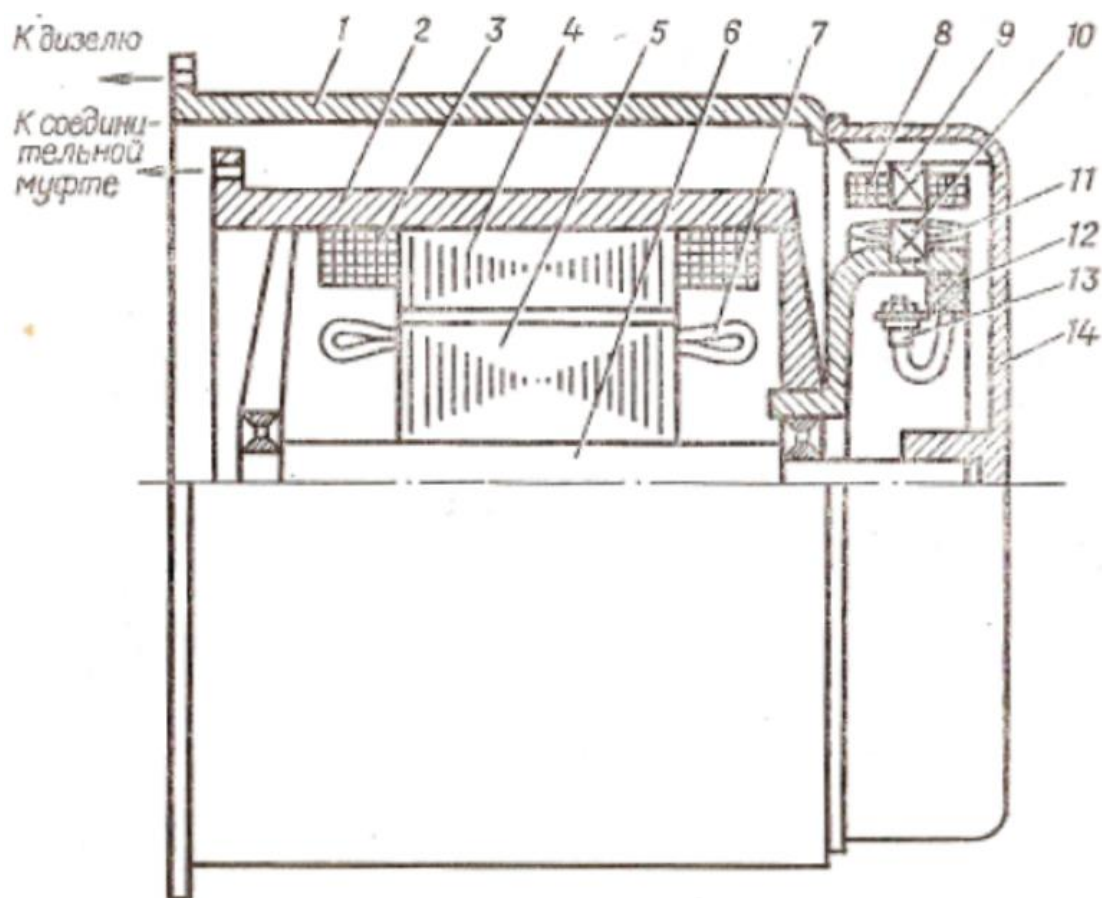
Маховичный синхронный генератор ГСМ: 1 – корпус генератора; 2 – индуктор (ротор); 3 – обмотка возбуждения; 4 – полюс; 5 – якорь (статор); 6 – вал; 7 – обмотка якоря; 8 – обмотка возбуждения возбудителя; 9 – полюс возбудителя; 10 – якорь (ротор) возбудителя; 11 – обмотка якоря возбудителя; 12 – обойма; 13 – диод; 14 – корпус возбудителя
